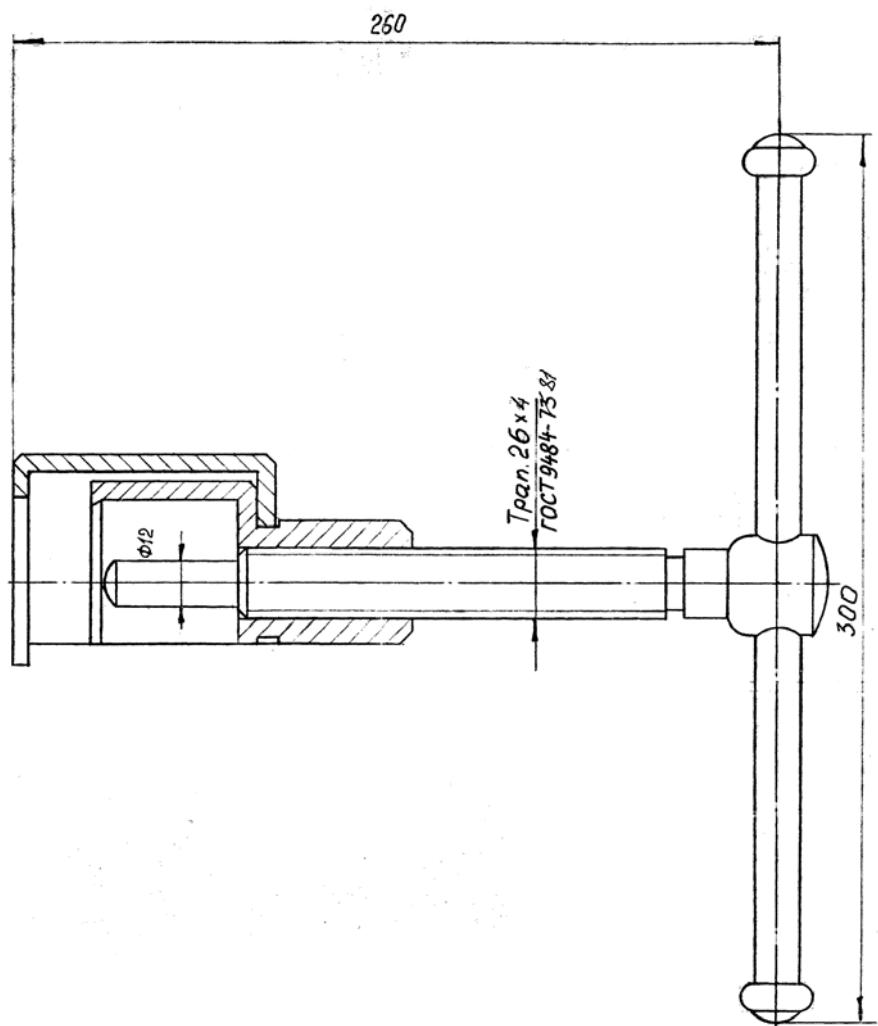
3М 7814-5118, Съемник звездочки и втулки коленчатого вала
